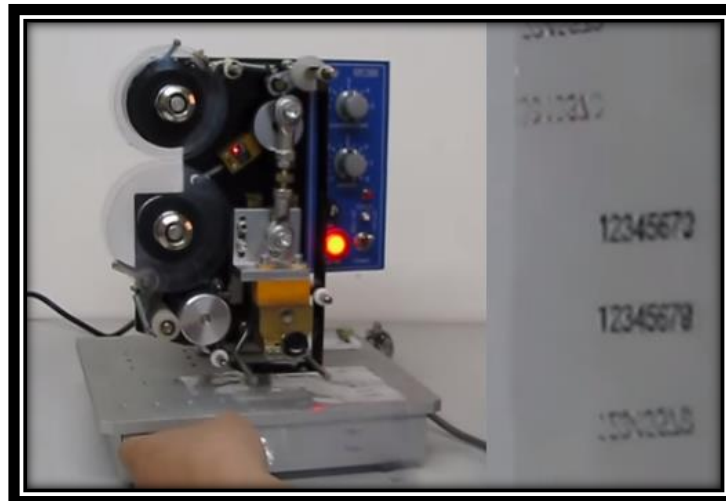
Impresora de Contacto/ Pruebas de impresión
